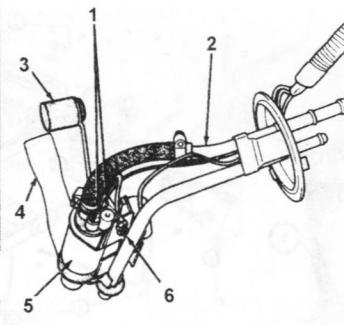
а Сборка топливного насоса и посылающего устройства на автосмбилях с СВКД
